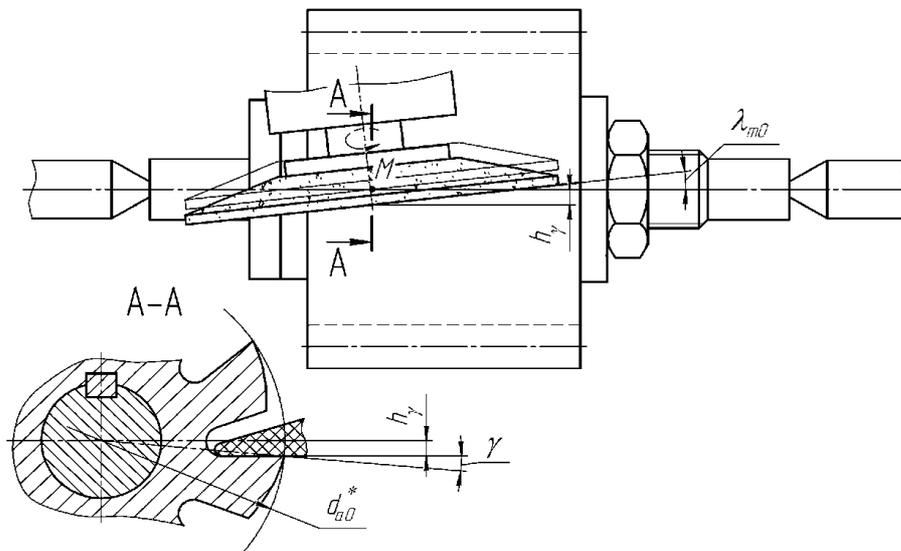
Схема заточки передней поверхности главной режущей кромки червячной фрезы
